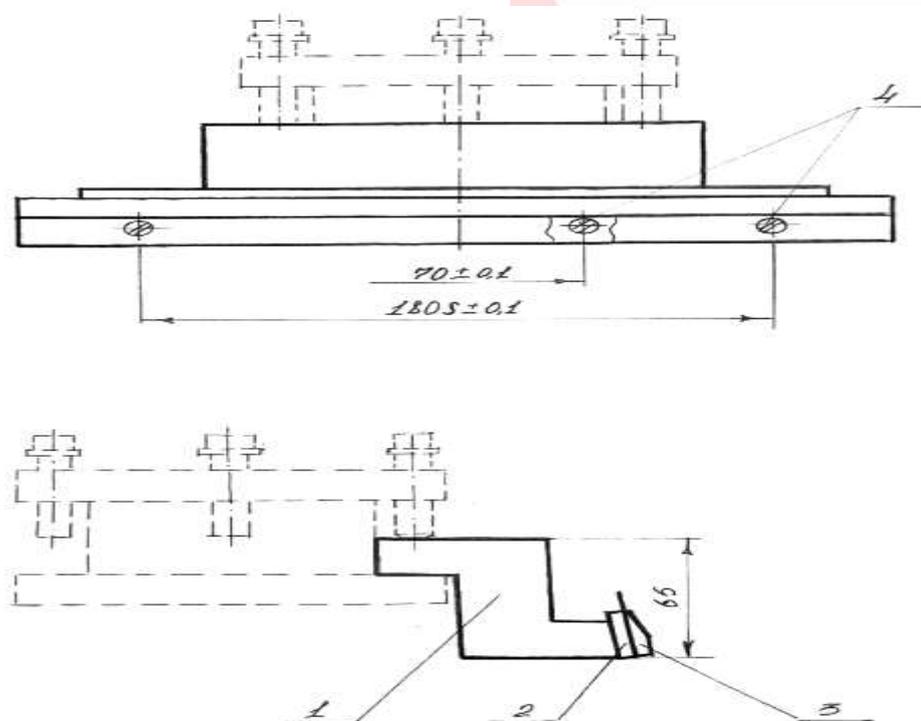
Ножедержатель: 1–корпус; 2–пластина корпуса; 3–пластина накладная; 4–винты.
